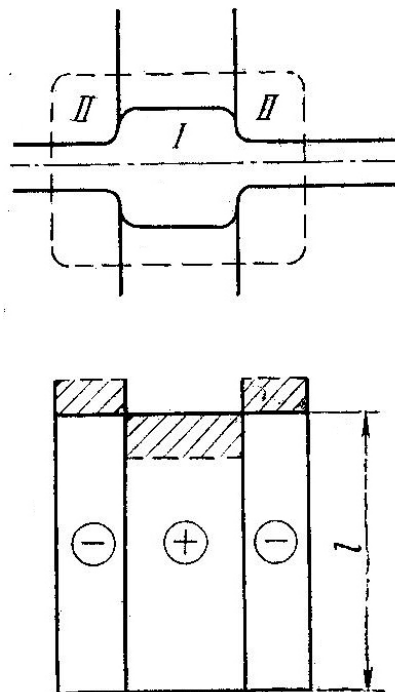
Схема прокатки крестообразного профиля из прямоугольной заготовки
